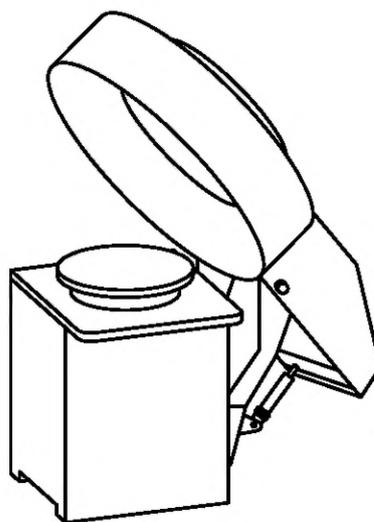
Кожух ротора для вертикального балансировочного станка (класс защиты В или С)
